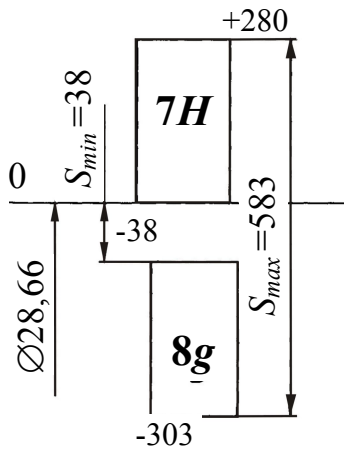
Схема полів допусків нарізного з'єднання
